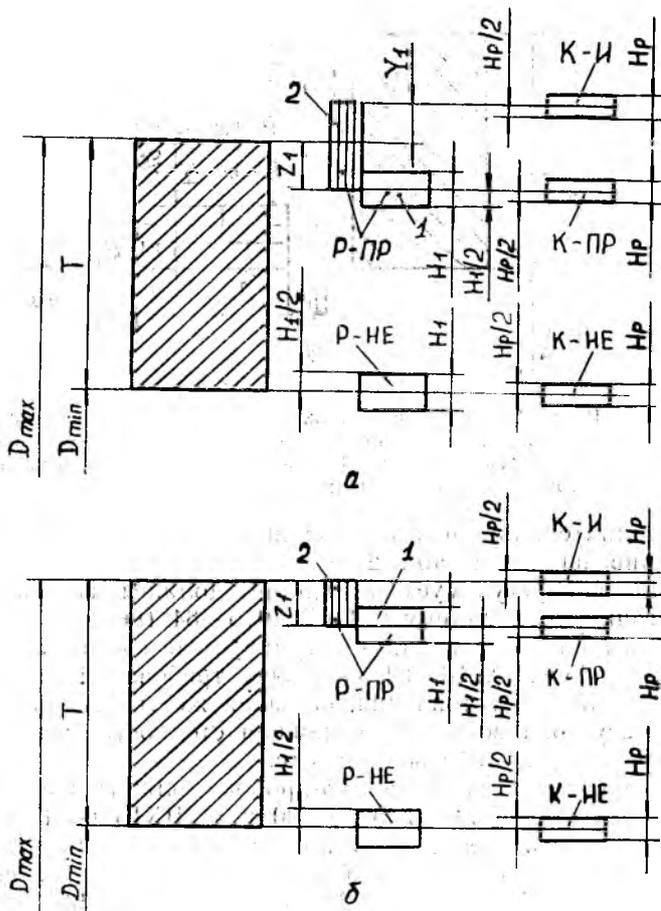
Схемы расположения полей допусков гладких калибров для валов квалитетов $IT6$ — $IT8$ (а) и $IT9$ — $IT17$ (б) номинальных размеров до 180 мм: 1 — поле допуска на неточность изготовления; 2 — поле допуска на износ
